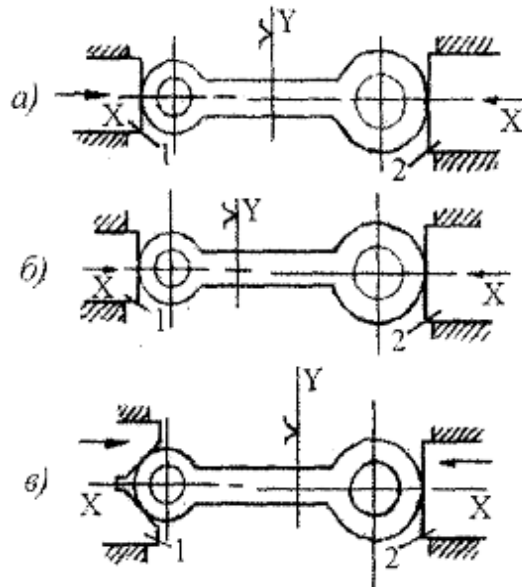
Закріплення заготовки при зустрічному русі двох направлених точкових затискачів
